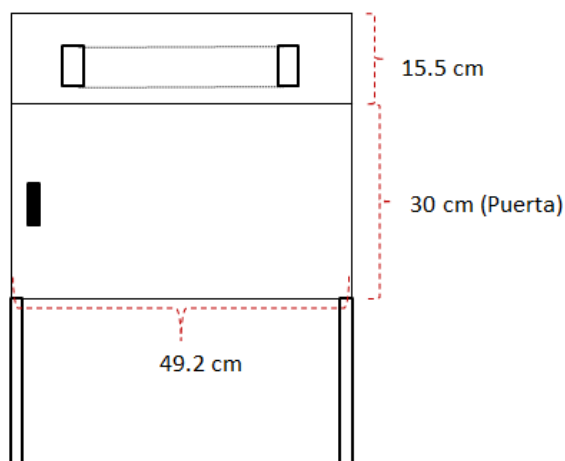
Dimensiones del deshidratador de 3kg parte frontal trasera.
